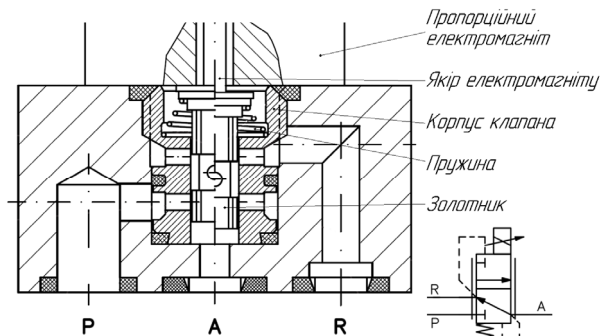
Конструктивне виконання і принципова схема пропорційного редукційного клапана
